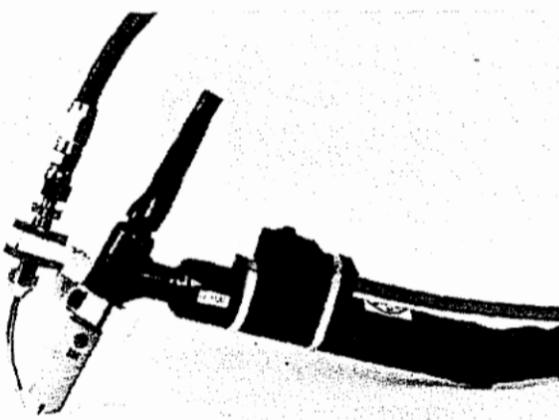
Горелка для полуавтоматической Аргонодуговой сварки
